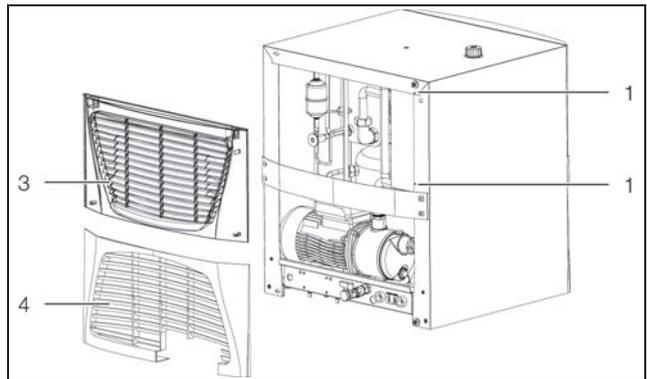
Predisposizione del collegamento PLC (3320.600 e 3334.600)
